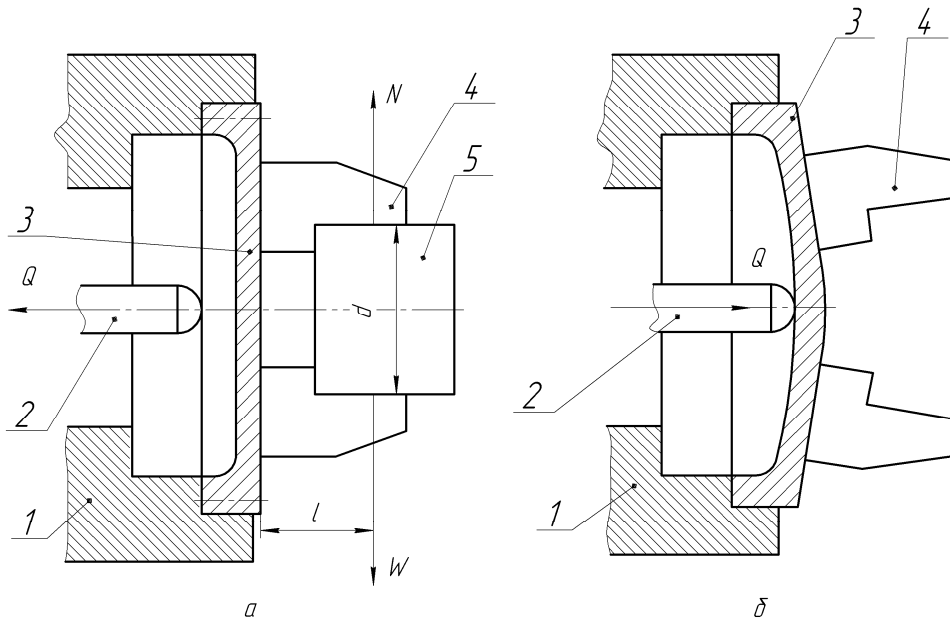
Будова й параметри різних положень мембранного патрона: 1 – корпус мембранного патрона; 2 – тяга; 3 – мембрана; 4 – кулачок патрона; 5 – оброблювана деталь; *a* – деталь, затиснута в мембранному патроні; *б* – патрон у розкритому положенні; *W* – радіальна сила на одному кулачку мембранного патрона; *Q* – зусилля на щитку; *d* – діаметр деталі; *L* – відстань від мембрани до середини кулачка
